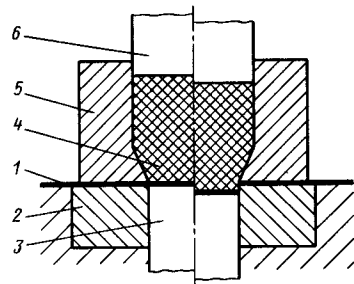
Схема пробивки отверстия в листе: 1 — заготовка; 2 — сменная матрица; 3 — прижим-выталкиватель; 4 — эластичная среда; 5 — контейнер; 6 — пулижер
